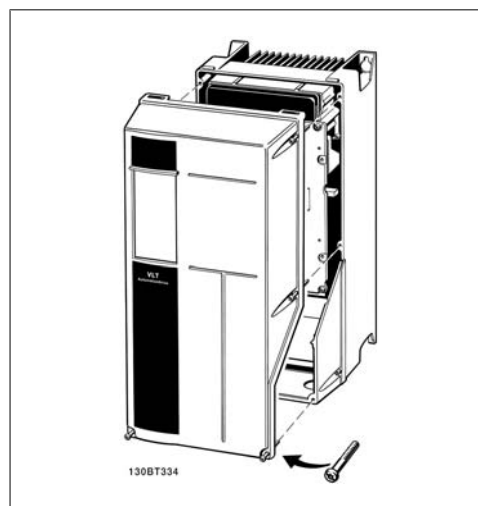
Корпуса A5, B1, B2 C1 и C2
